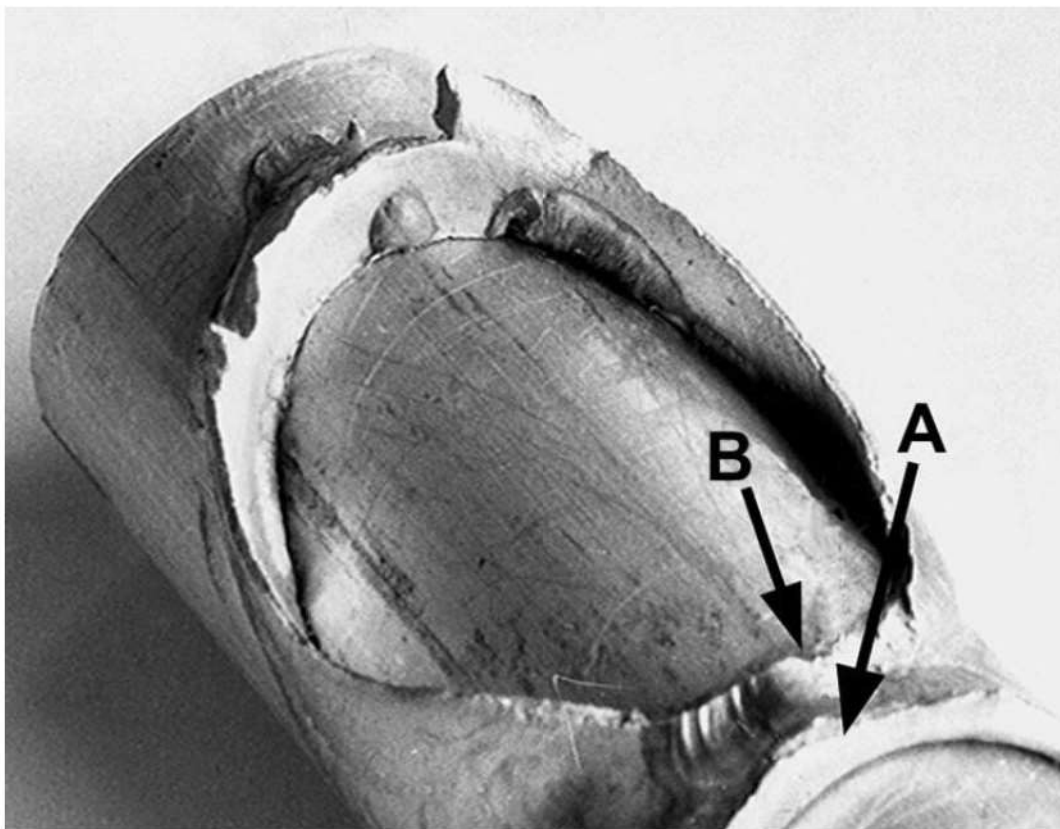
Aspecto de la región fracturada del tubo (3) vista desde otro ángulo, mostrando la presencia de solapamientos de soldadura. Las flechas A y B apuntan para los locales de inicio de la fractura.
